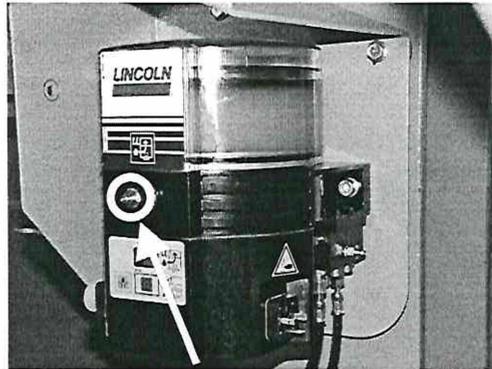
Бак смазки со смазочным ниппелем для заправки бака
